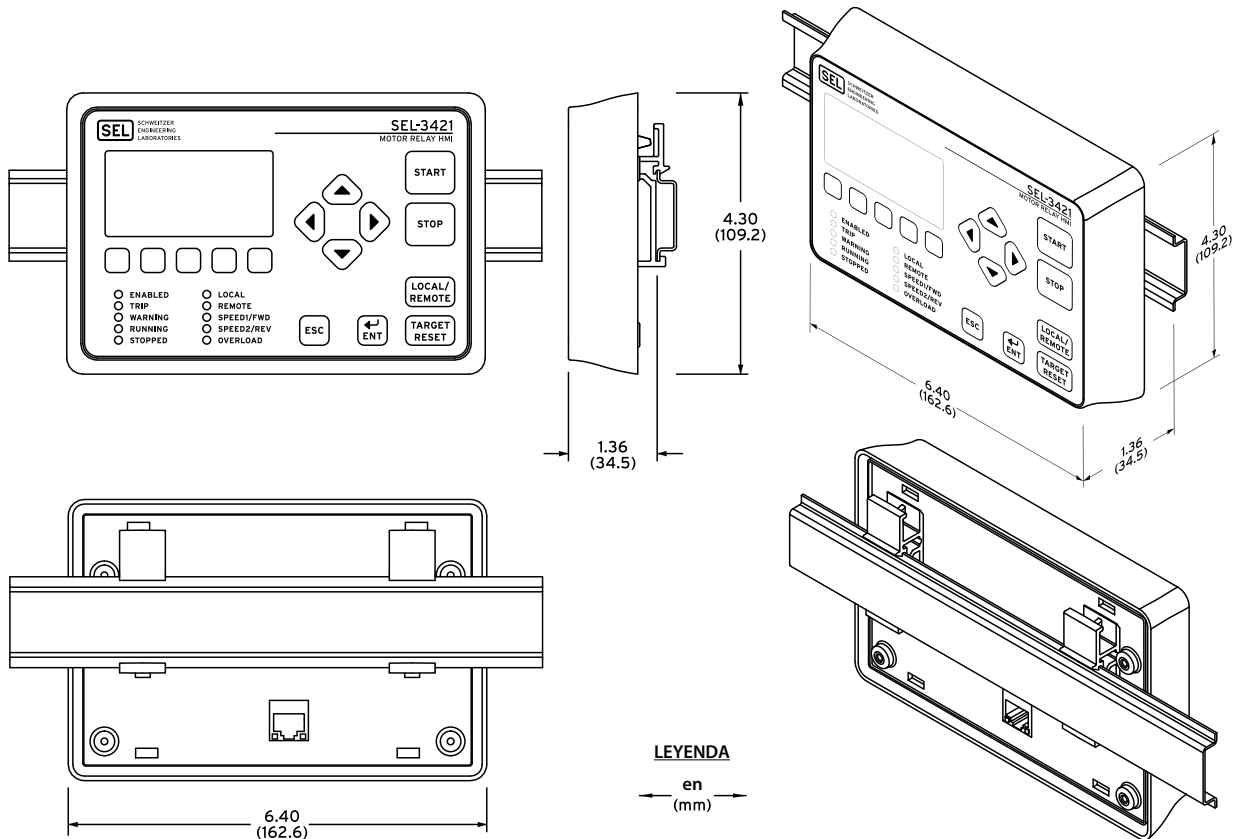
Dibujos de la Instalación de la IHM del Relé de Motor SEL-3421 (Montaje en Riel DIN)
